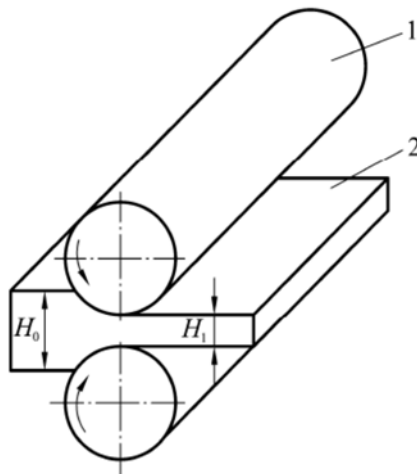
Схема процесу поздовжньої прокатки
